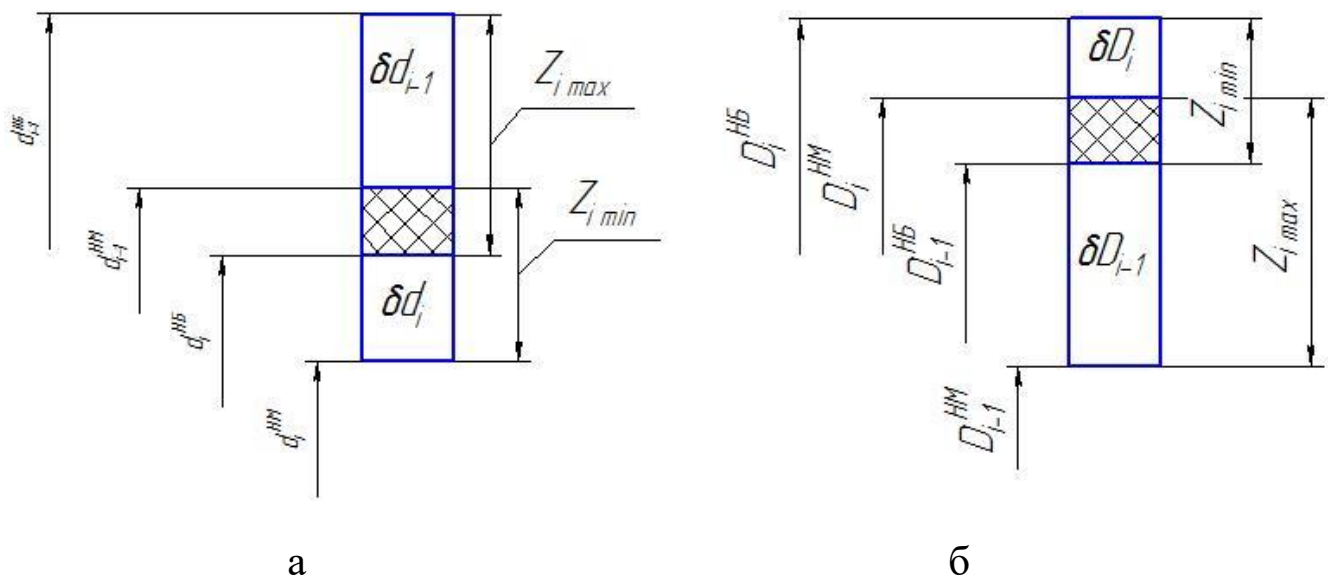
Схема розташування припусків і допусків для поверхонь: а) – охоплюваної; б) – охоплюючої.
